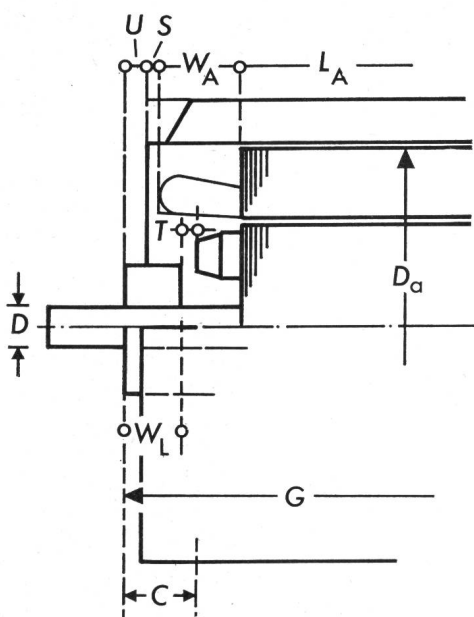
Zur Berechnung der Gesamtlänge der oberflächengekühlten Motoren
